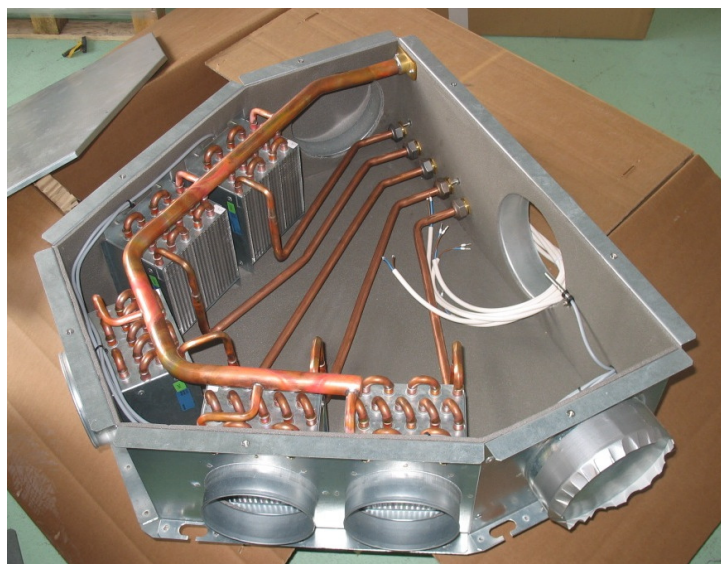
Vue de côté avant gauche du nouveau prototype
